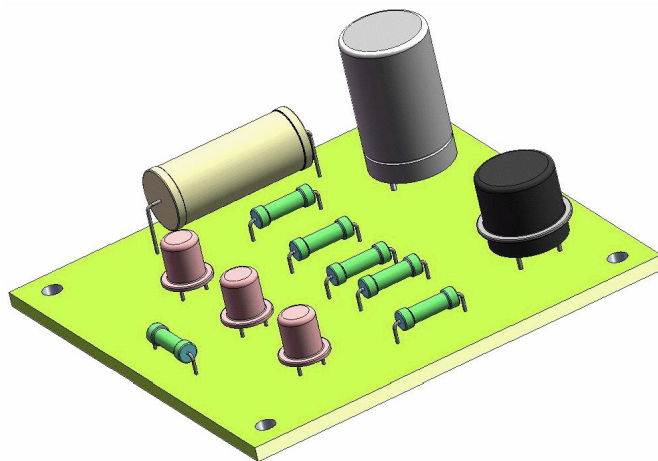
Трехмерная модель линейного стабилизатора напряжения
